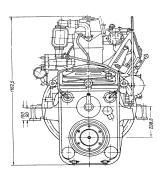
Вид со стороны реверс-редуктора Fig. 6 — View from reversing reducer
